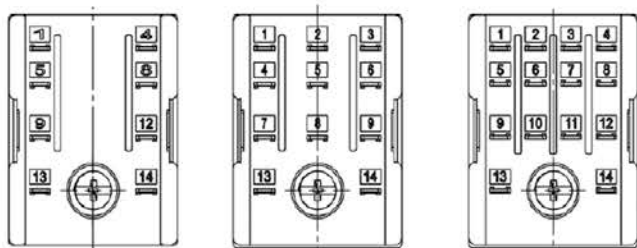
Габаритные, установочные, присоединительные размеры реле OptiRel G RP55-1X для монтажа на печатную плату с кнопкой «Тест».
